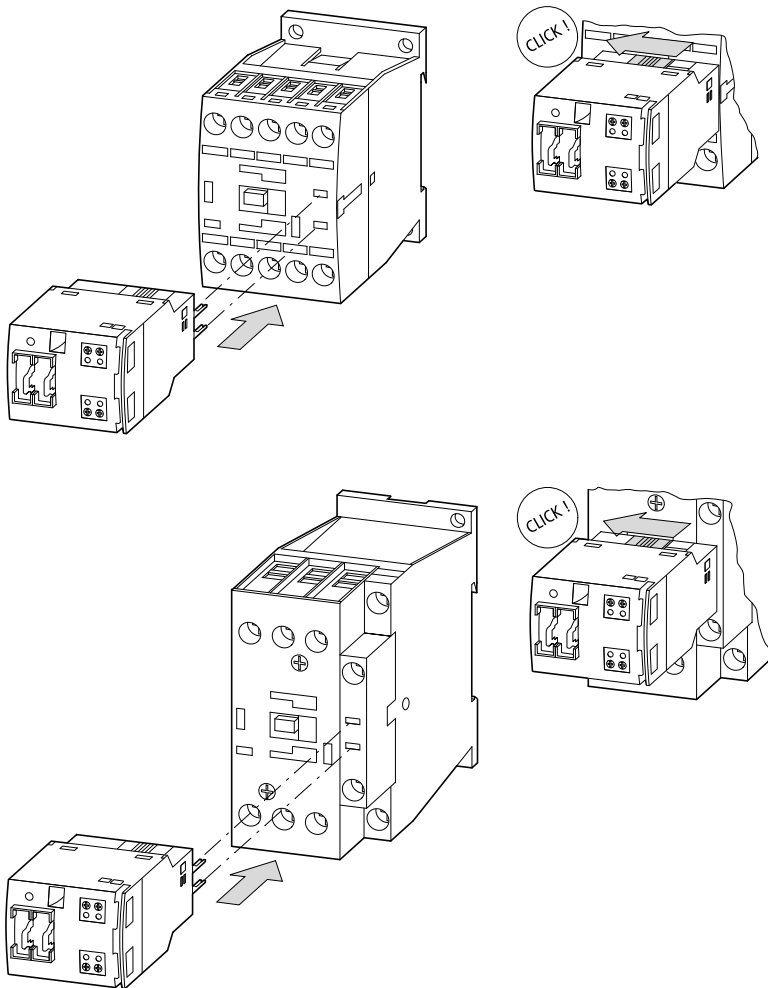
Montaggio modulo SmartWire per DILM e contattore
